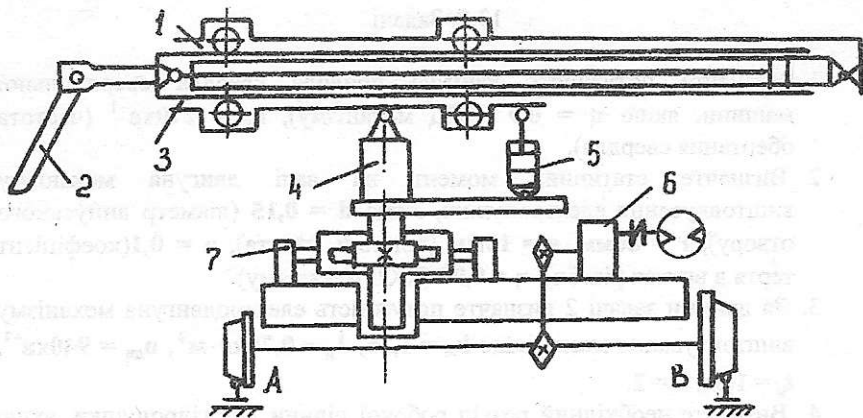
Схема опіковочної машини: 1-направляюча рама; 2-піка; 3-штанга; 4-поворотна колона; 5-циліндр нахилу стріли; 6-механізм переміщення; 7-пневмоциліндр повороту колони
